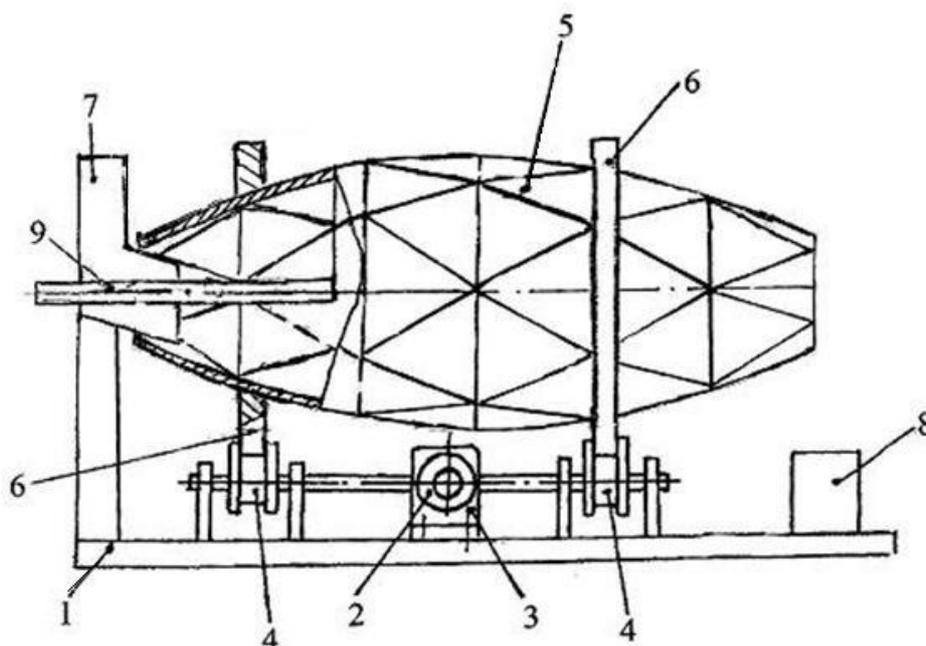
Устройство для приготовления растворов и бетонных смесей, общий вид (1 – станина, 2 – электродвигатель; 3 – редуктор; 4 – четыре роликовые опоры; 5 – барабан; 6 – два обода барабана; 7 – устройство для загрузки; 8 – устройство для разгрузки; 9 – трубопровод)
